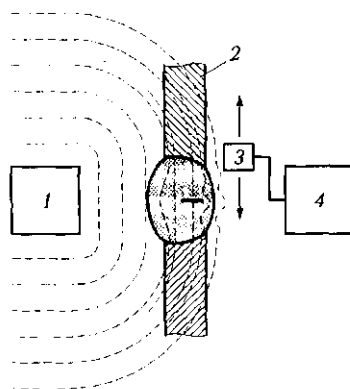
Схема контроля сварного соединения методом вихретоковой дефектоскопии:
